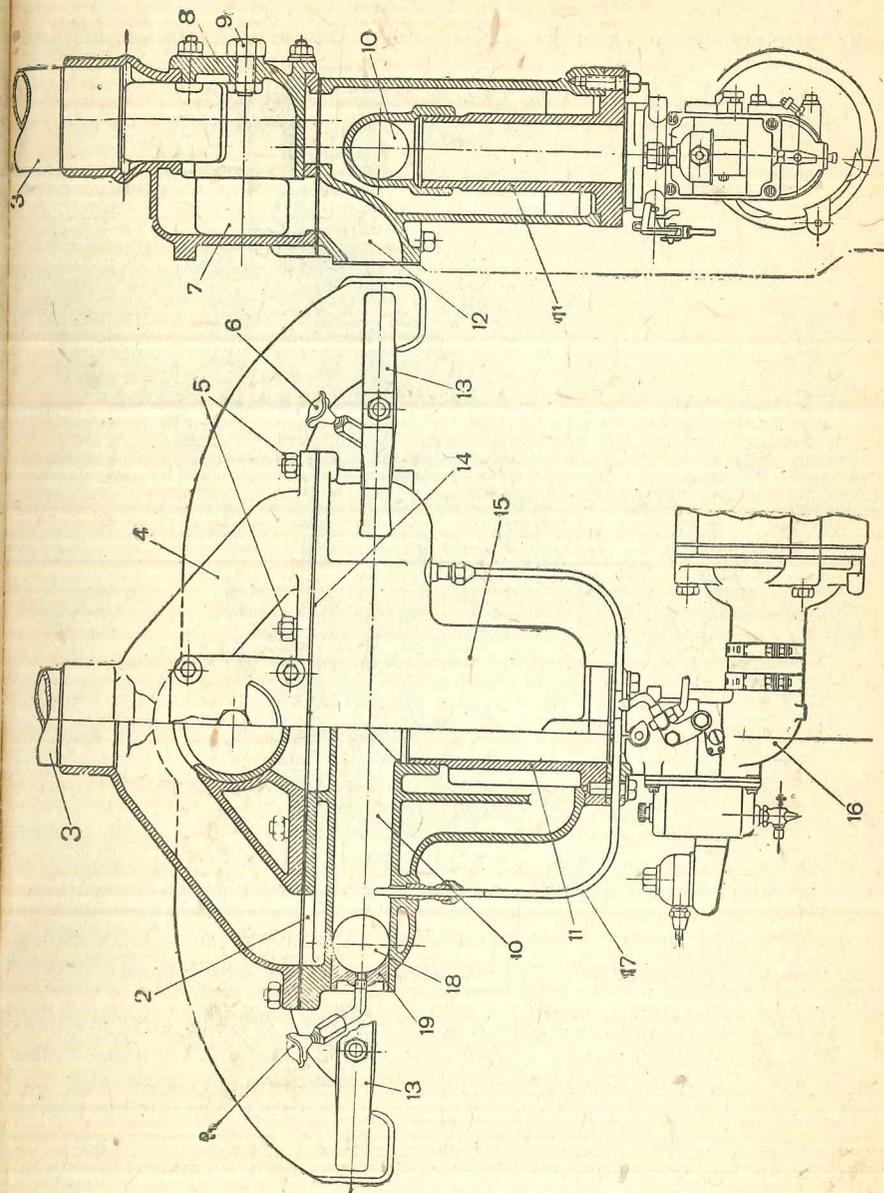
Разрез всасывающего и выхлопного коллектора.
